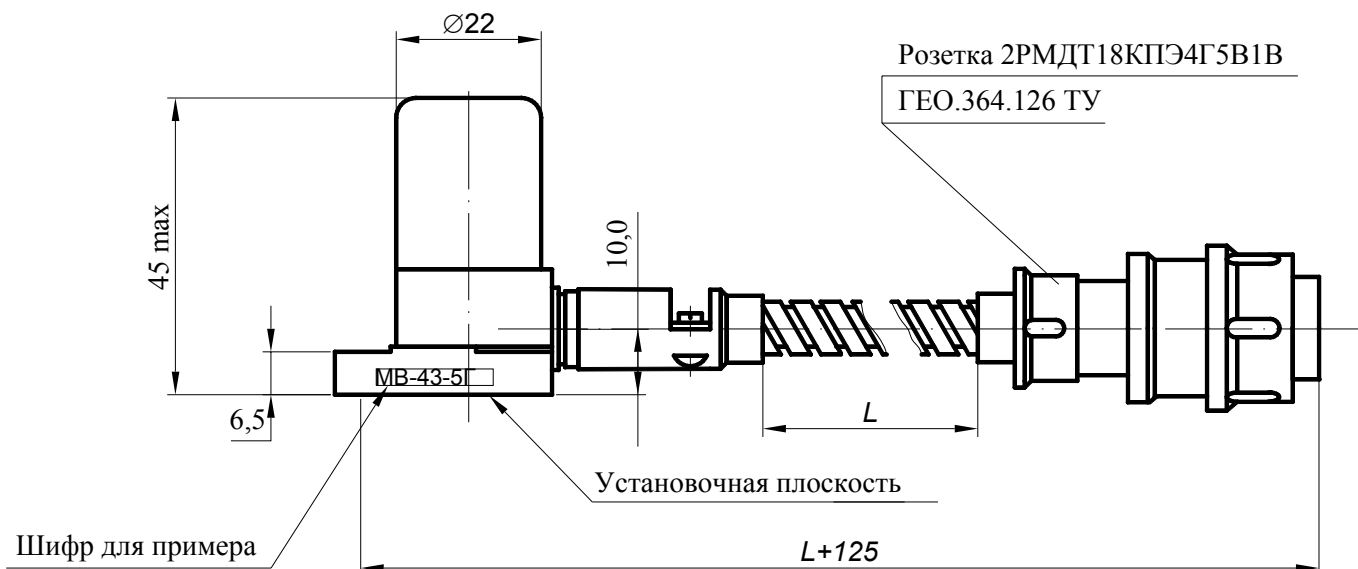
Габаритно-установочные размеры вибропреобразователя MB-43-5Г/L
